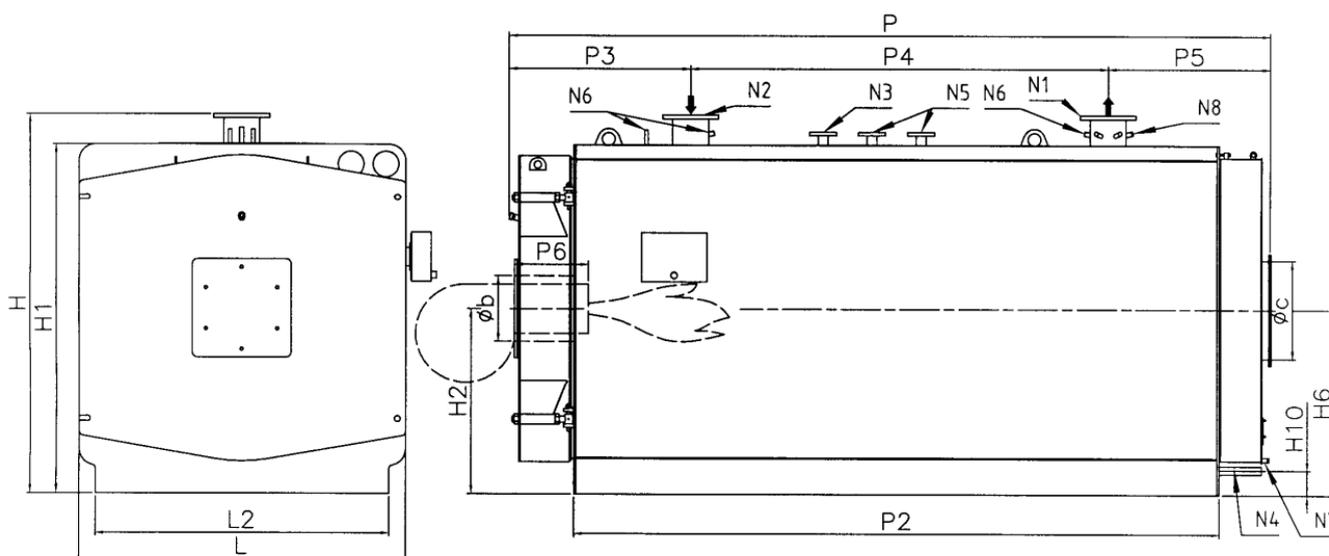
Устройство котла Ici Caldaie REX-3000
